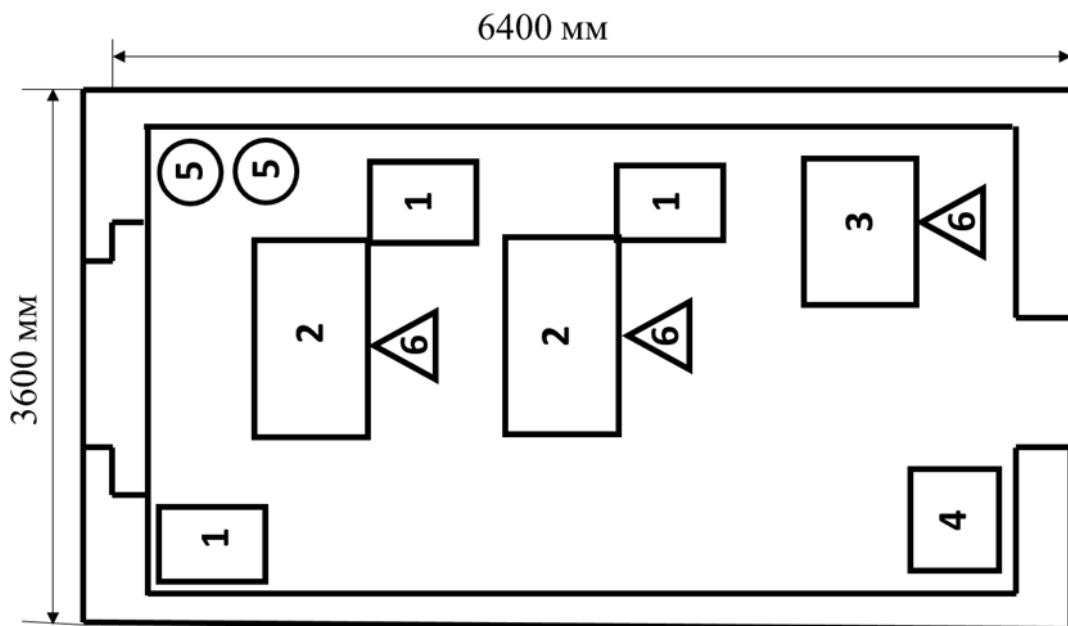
Электротехнический участок по изготовлению стеклянных плавких предохранителей: 1 – рабочий стол; 2 – установка инфракрасной заварки плавких вставок; 3 – установка контактной сварки; 4 – сейф; 5 – баллон с инертным газом; 6 – рабочее место монтажника РЭА и приборов
